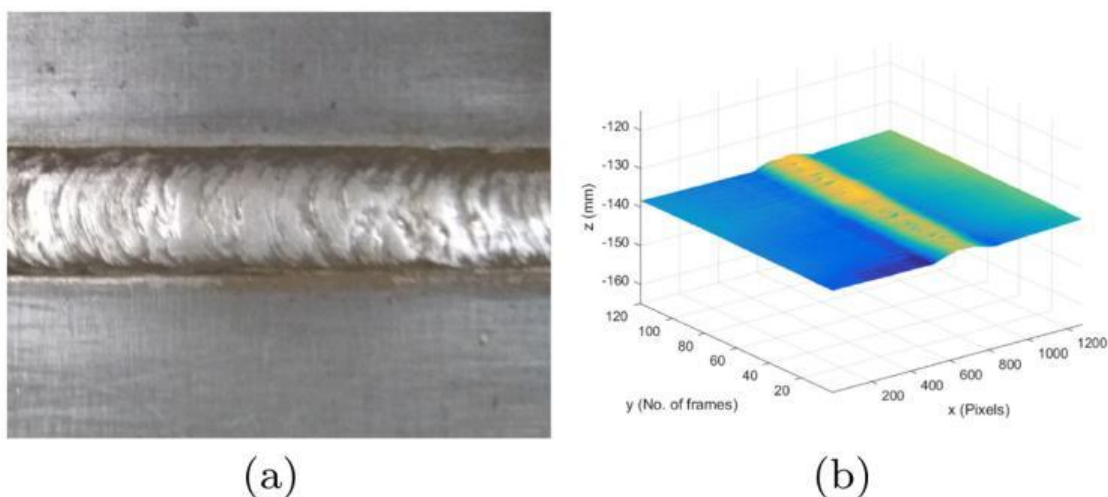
Участок сварного шва: а) собственно сварной шов, б) его 3D-реконструкция [8]
